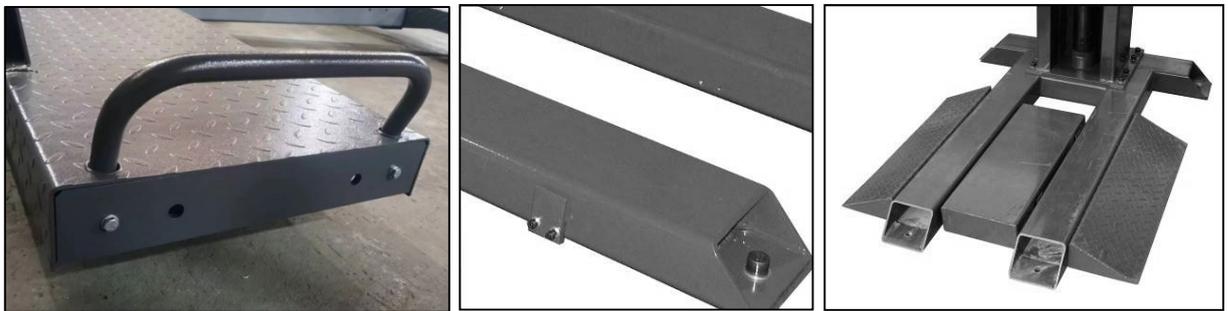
, 12, 13 Protección antivuelco y rampa de acceso
